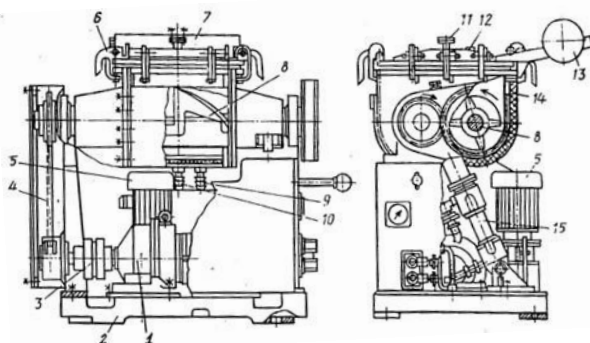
Двухроторный смеситель с Z-образными лопастями:
